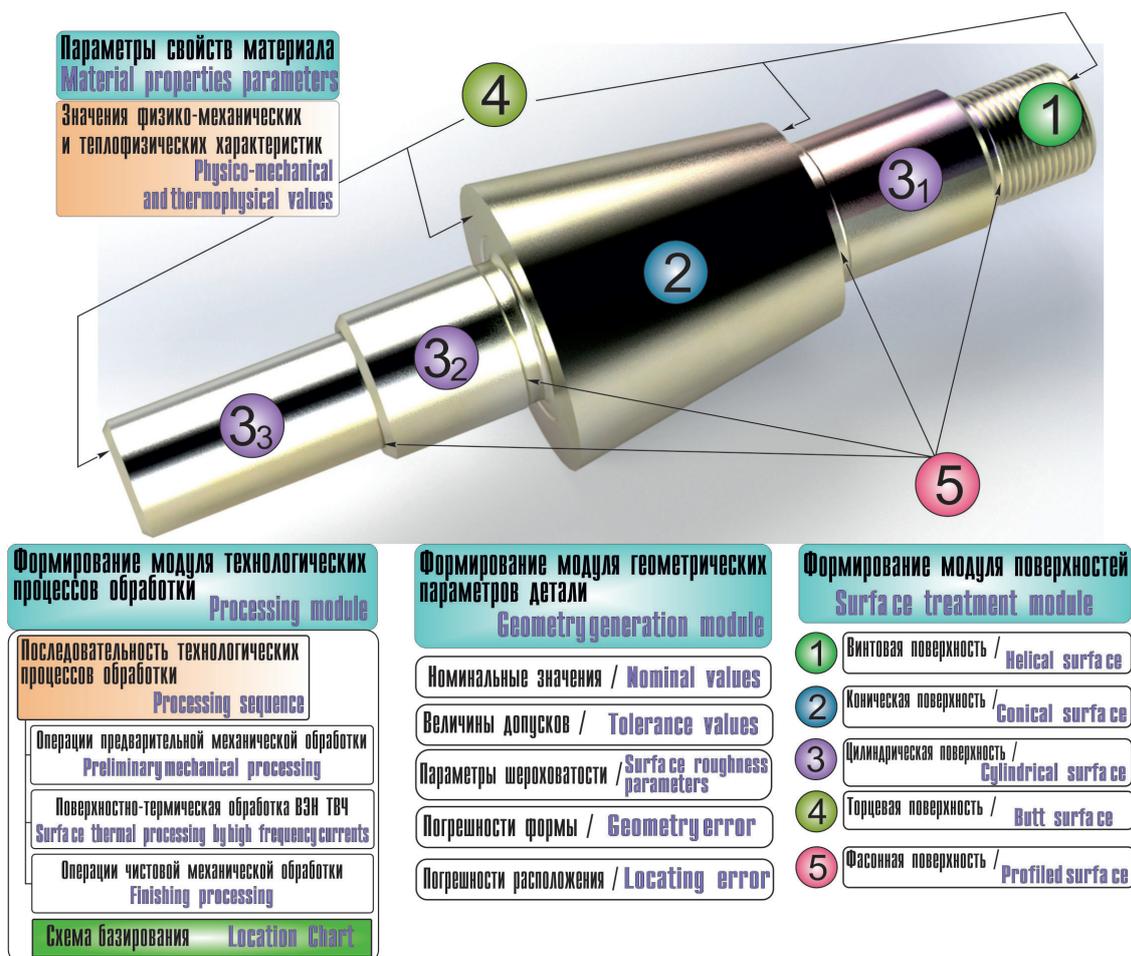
Разложение обрабатываемой детали типа «Вал» на элементарные поверхности
